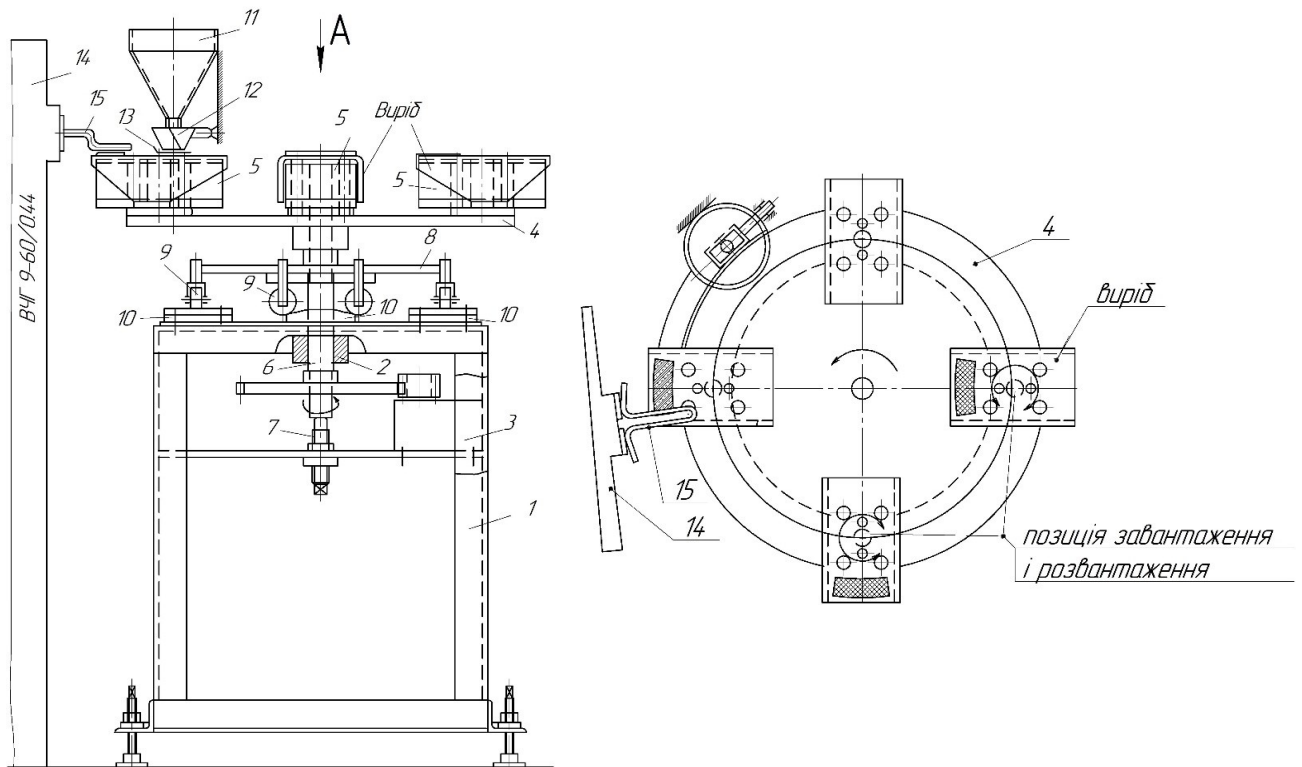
Схема напівавтомата для індукційного наплавлення [68]:
